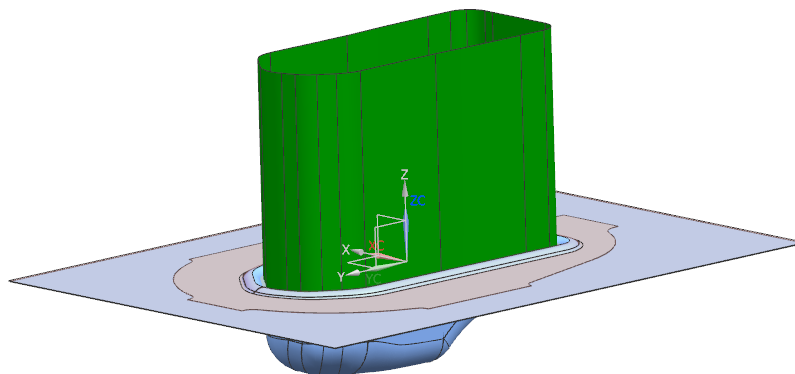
Ассоциативные копии поверхностей рабочего инструмента и заготовки
